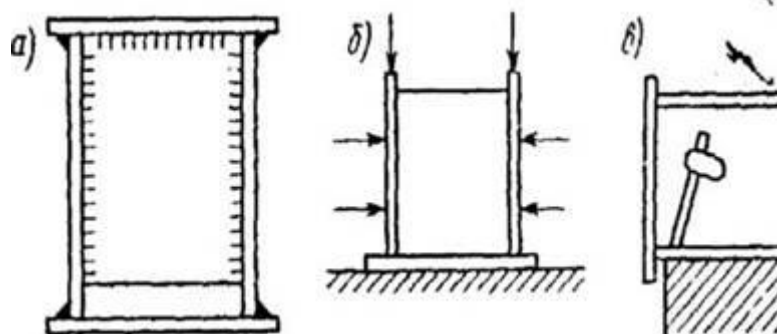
Изготовление балок коробчатого сечения: а - сечение балок; б - установка боковых стенок; в - сварка внутренних швов
